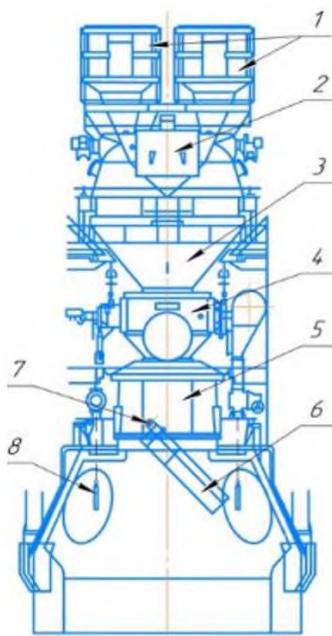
Общий вид бесконусного загрузочного устройства
